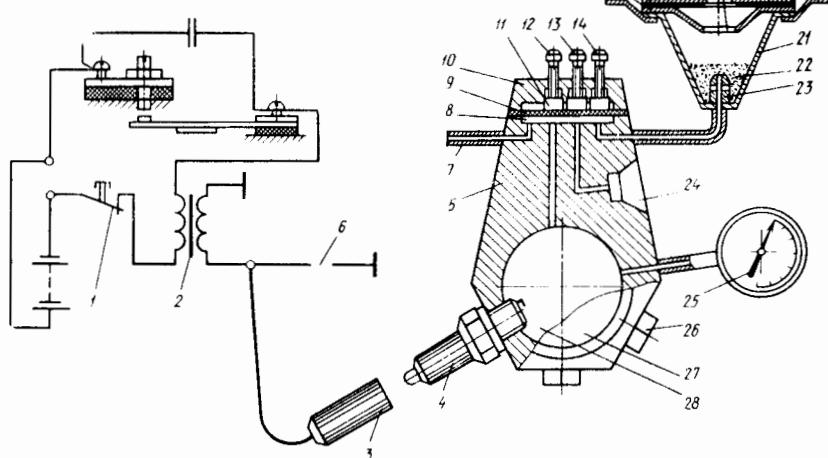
Схема прибора мод. 514-2М для очистки и проверки искровых свечей зажигания:
